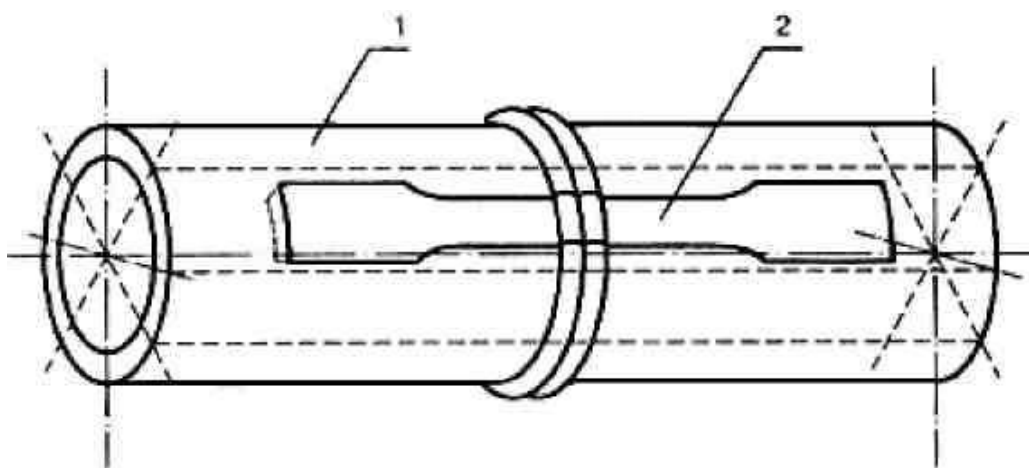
Схема вырезки образцов из сварного соединения для испытания на осевое растяжение: 1 – патрубок со сварным соединением; 2 – расположение образцов
